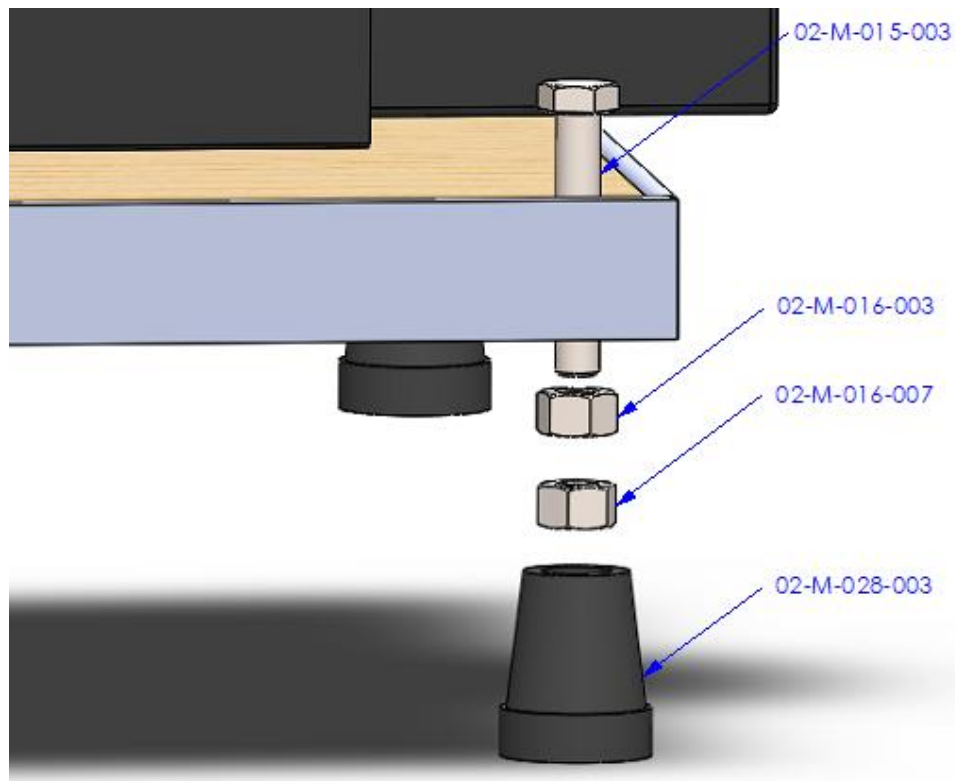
Vista explosionada de los apoyos regulables en altura.
